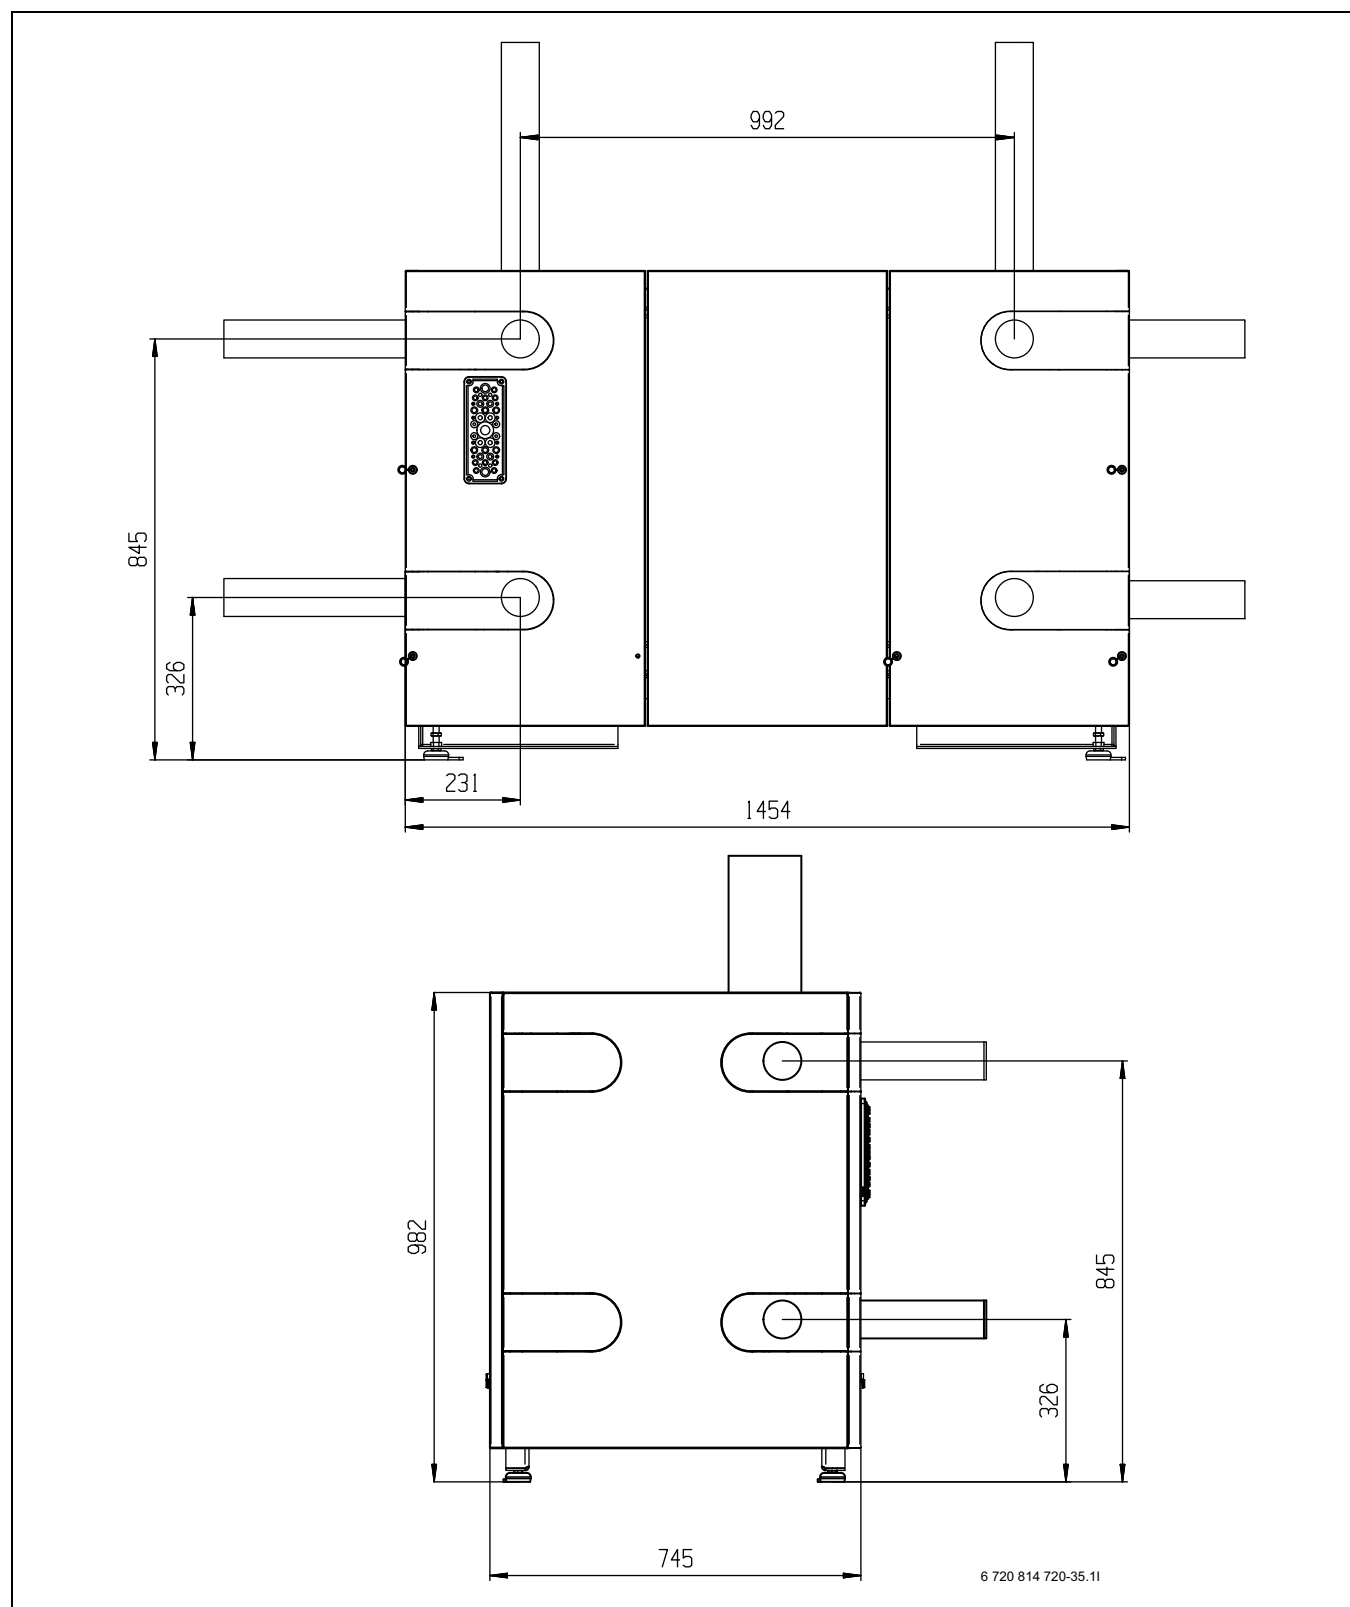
Dimensions de la pompe à chaleur (54–80 kW)
